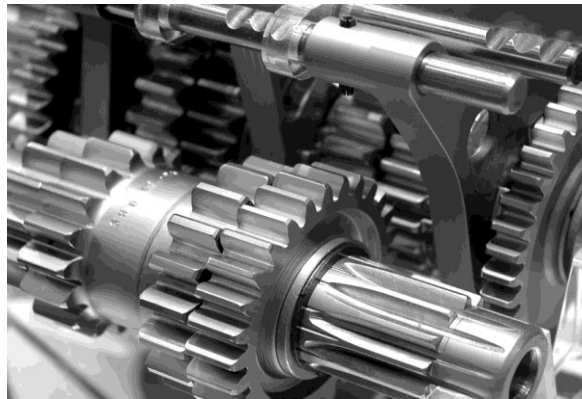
Коробка швидкостей з зубчастими високошвидкісними колесами
